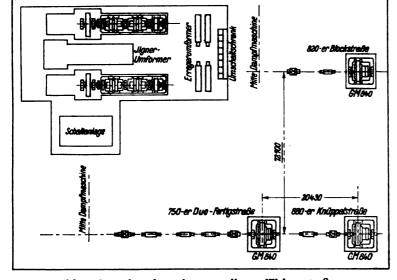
Lageplan der schwungradlosen Walzenstraßen.
